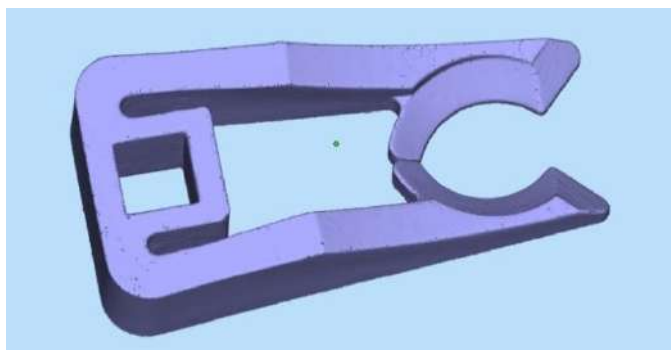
3D-модель фиксатора заготовок (Тип 1)
